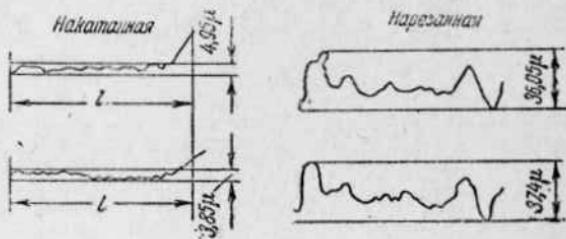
Поверхность резьбы, накатанной плашкой.
